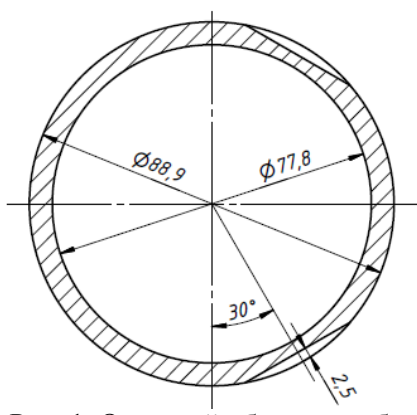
Опытный образец трубы КСМ типоразмера НQ
